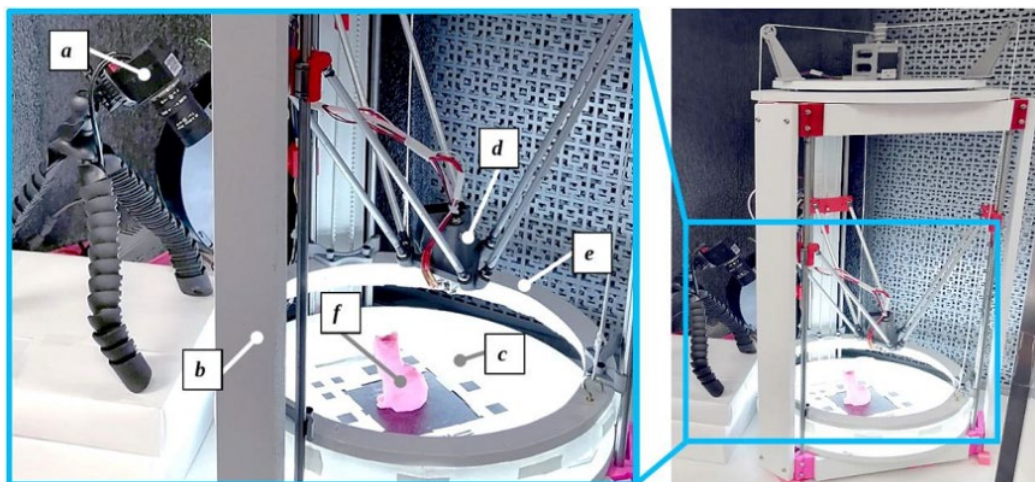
Платформа визуального обслуживания: рабочая зона (слева), сборка принтера (справа): а — камера; b – каркас 3D-принтера; c – табличка визуальной разметки сверху печатной платформы; d – экструдер; e – подвижный осветительный каркас; f – печатная часть
